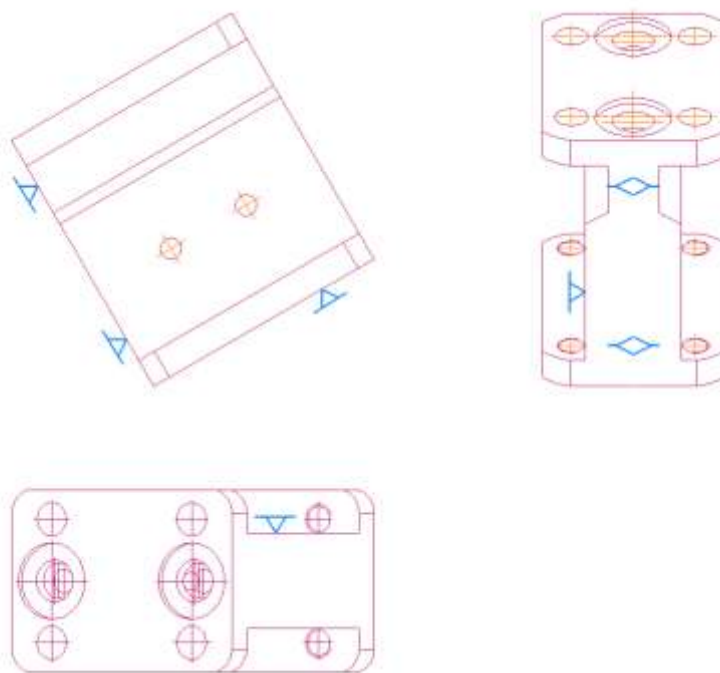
Схема теоритического базирования заготовки в разрабаты-
